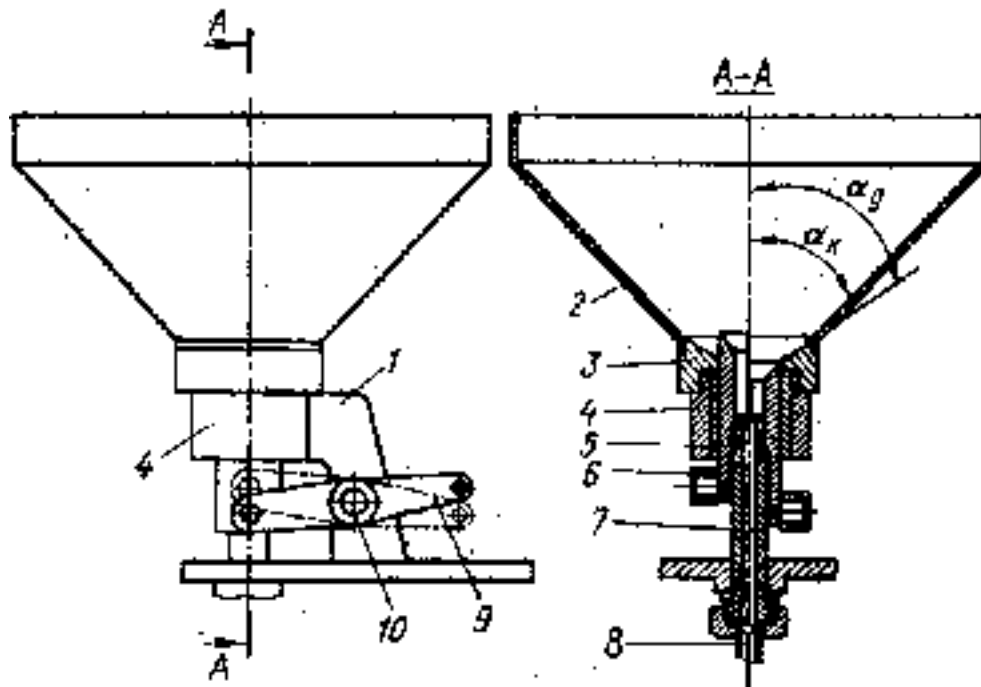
Конструкция бункера с захватно-ориентирующими двумя подвтулками
